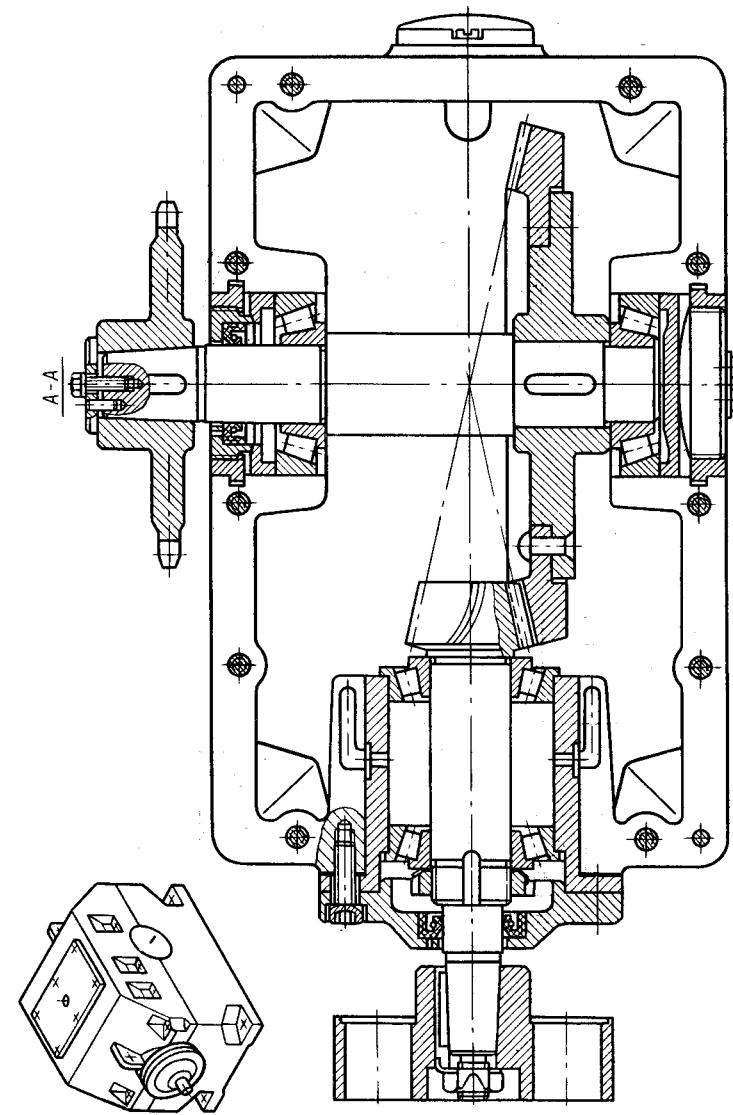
Редуктор конический одноступенчатый горизонтальный
